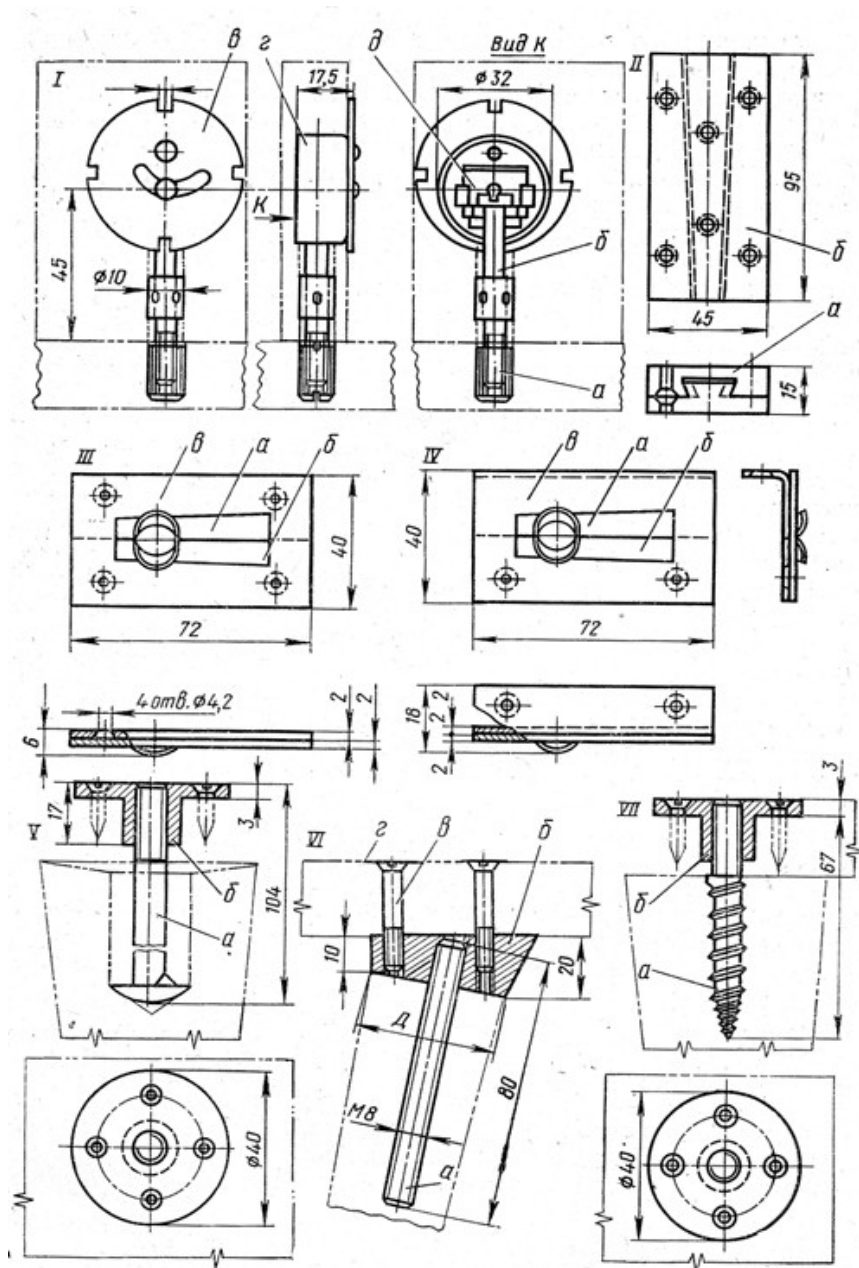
Загальний вигляд та будова різних моделей стяжок: I – ексцентрикова універсальна; II – клинова; III – клинова з натяжною рамою; IV – клинова кутова; V – болтова; VI – гвинтова; VII – гвинтова з глухарем. [5]
